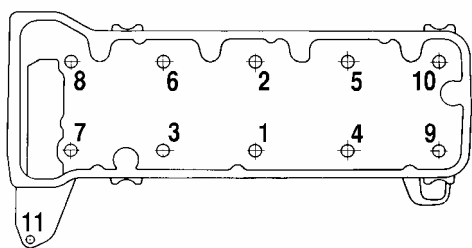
Порядок затягивания болтов головки цилиндров
